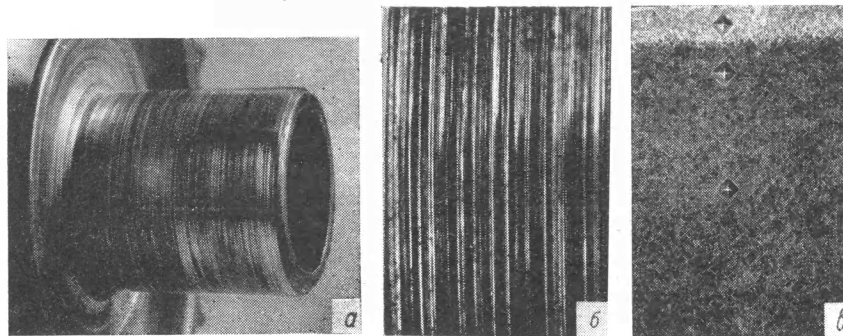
Шейка двойной шестерни привода нагнетателя авиационного двигателя после 600 ч работы:
